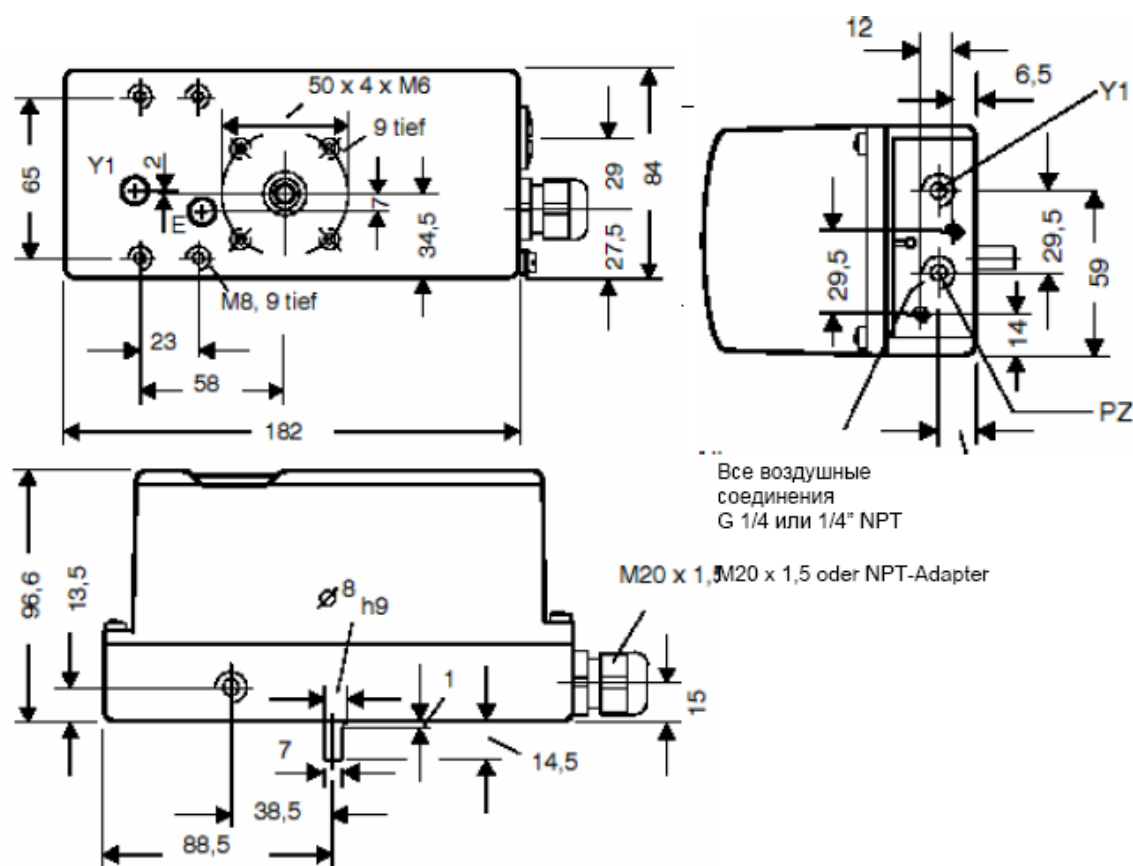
Габаритный чертеж конструкции в металлическом корпусе 6DR5xx1
